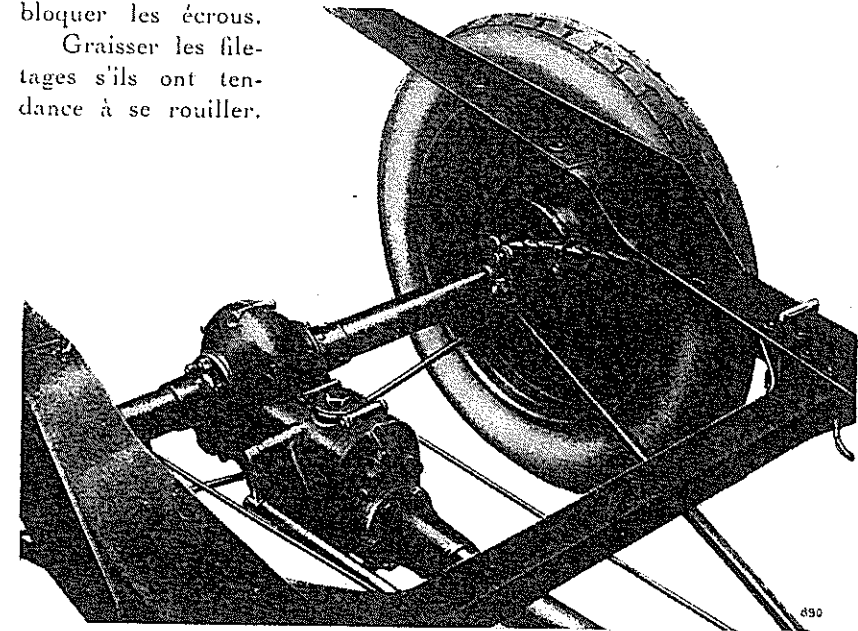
PARTIE ARRIÈRE DU CHASSIS.
